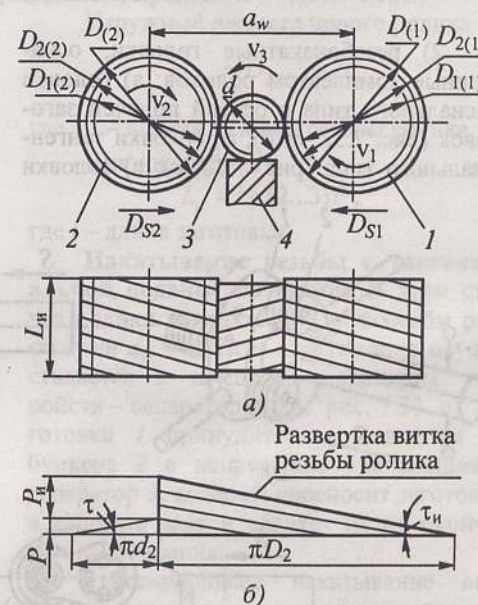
Схема накатывания резьбонакатными роликами:
